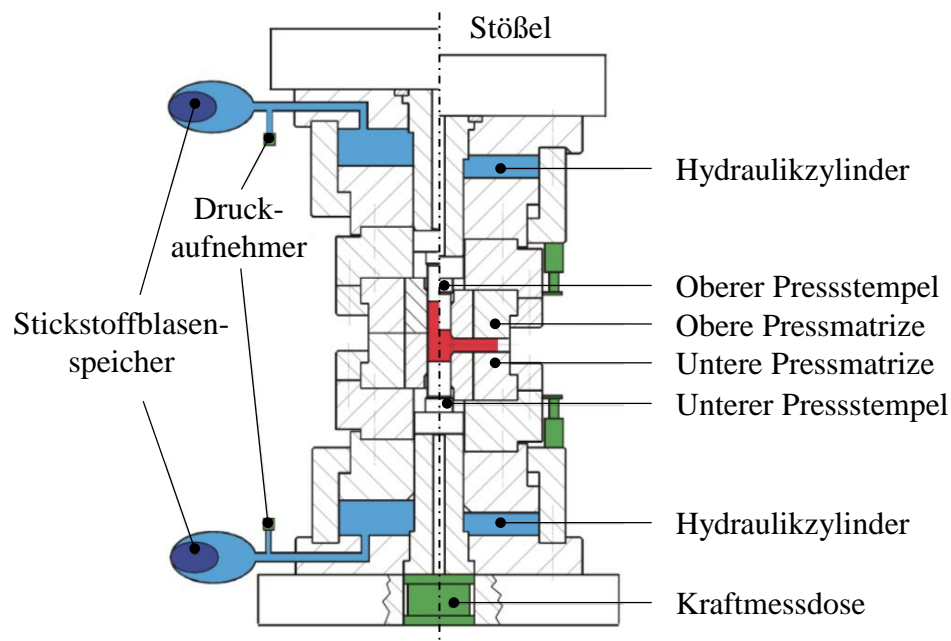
Aufbau einer Schließvorrichtung mit integriertem Querfließpresswerkzeug [25]
